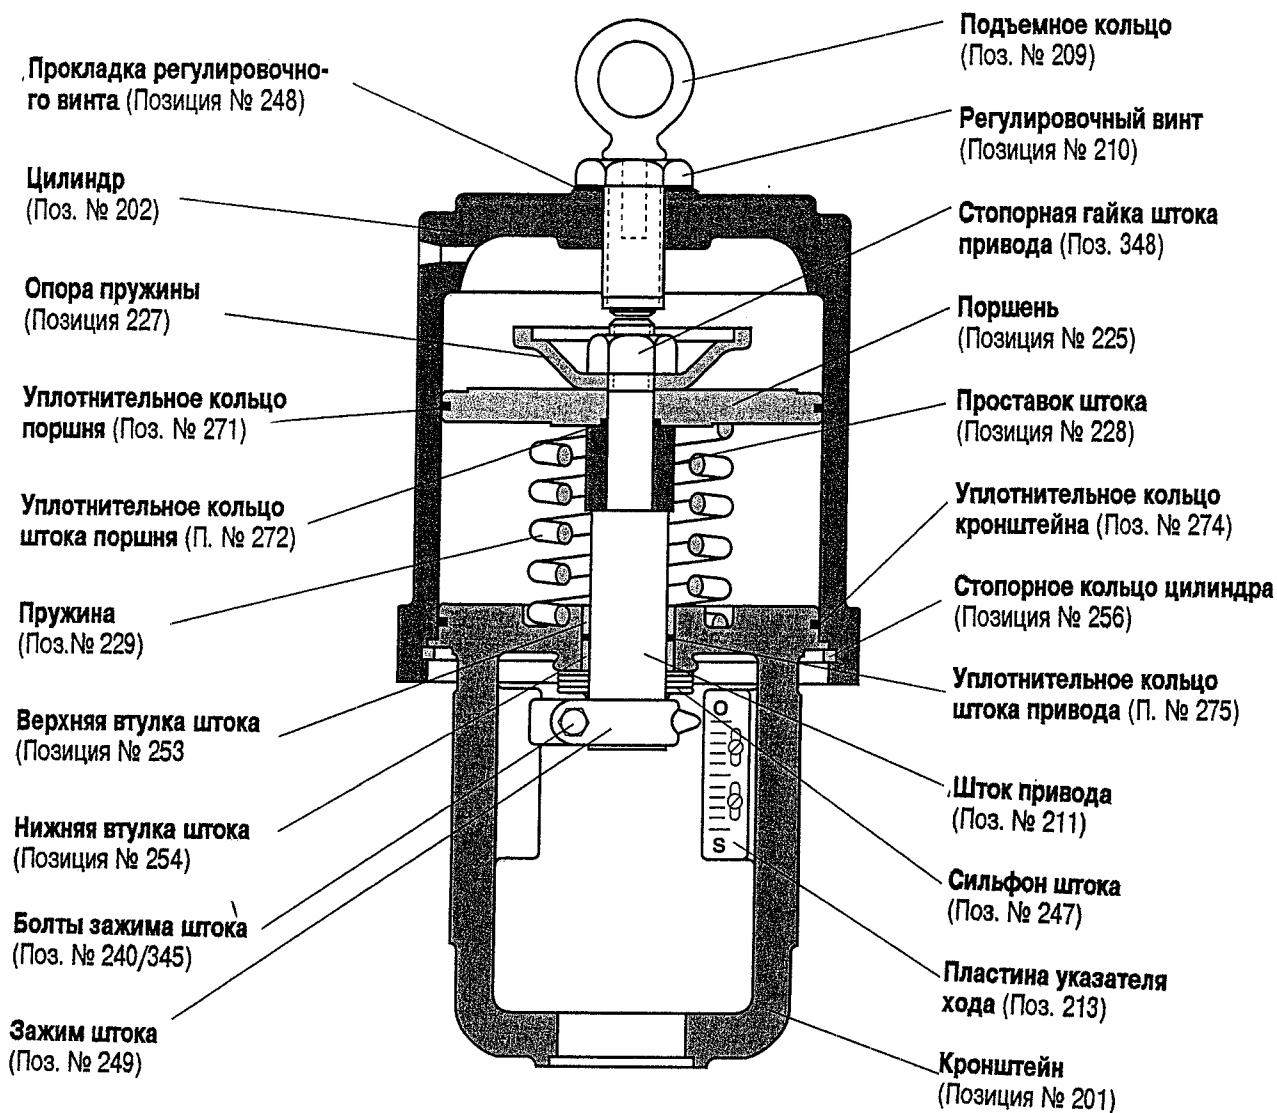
Цилиндр привода с выдвигающимся под давлением воздуха штоком
